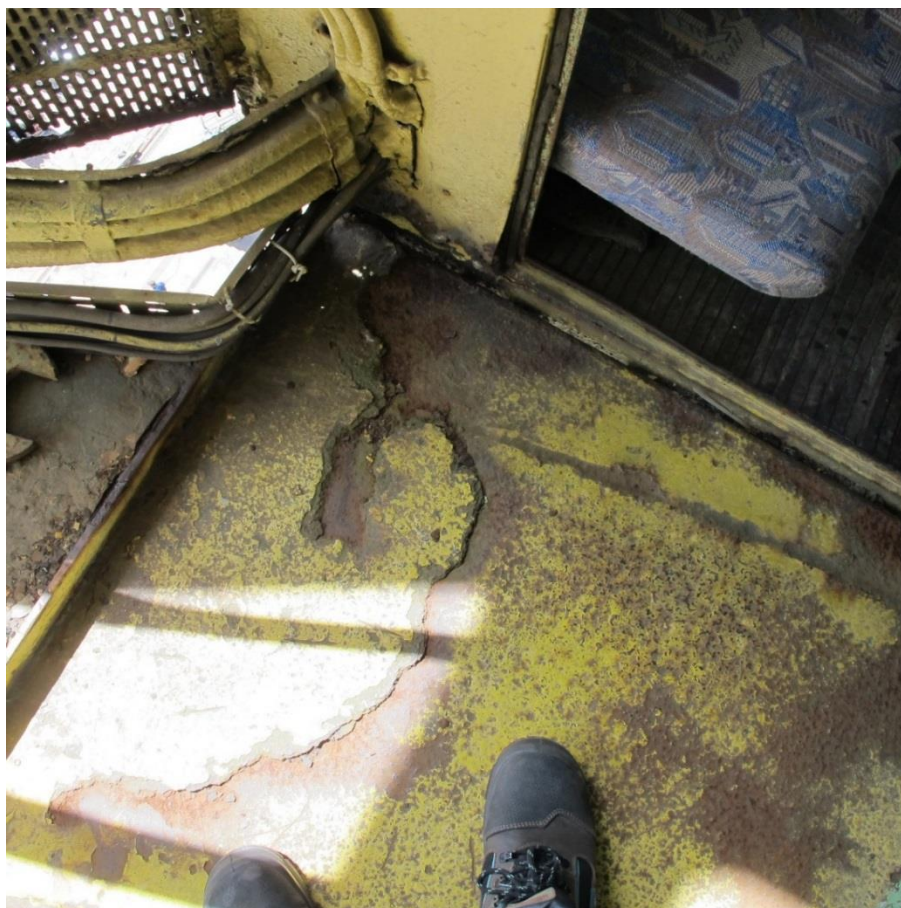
Pęknięcia zmęczeniowe kolumny obrotowej podestu ruchomego zainicjowane korozją elementu.
